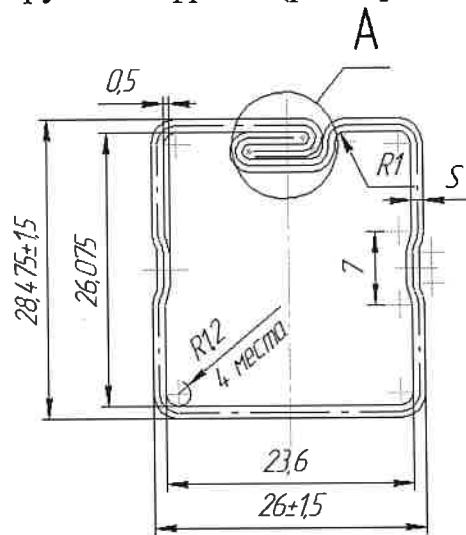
Труба с гофрами (размер заготовки 124 мм)
